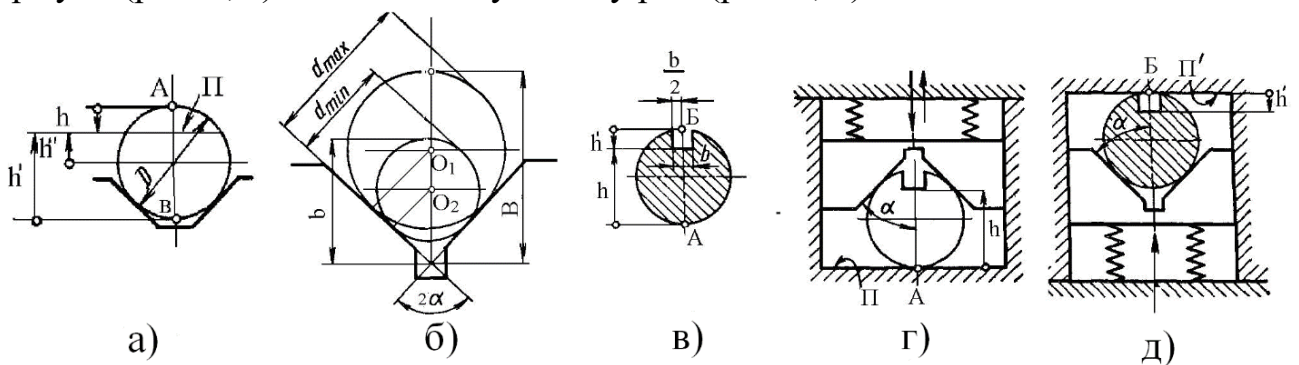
Схеми визначення похибки установки деталей по зовнішньої циліндричної поверхні
